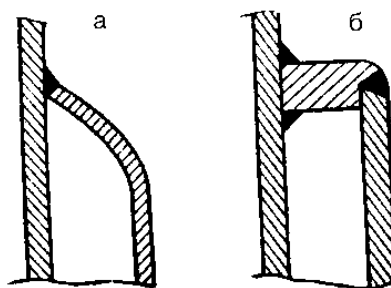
Способы приварки рубашки к корпусу аппарата:
